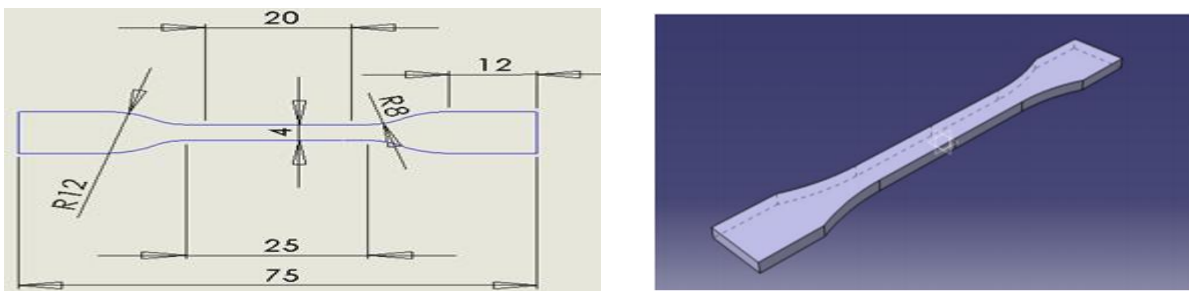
dimensions des éprouvettes selon la norme ASTM D638-03[6]
